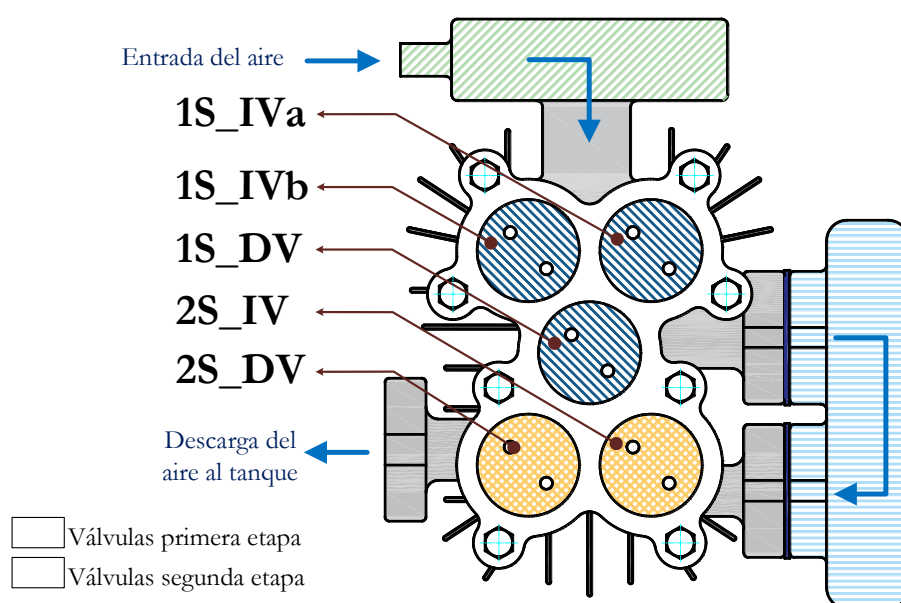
Vista superior del cabezote del compresor. Fuente: Propia.
